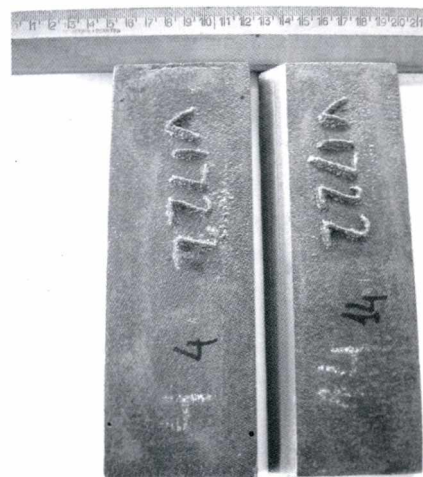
Detalle del maquinado de la junta para realizar la soldadura
